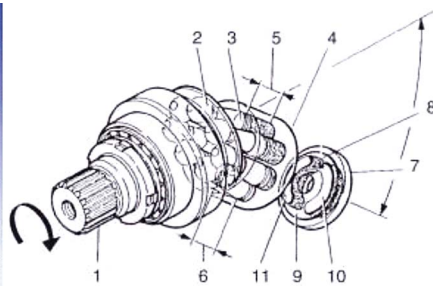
Нерегулируемая машина Bosch Rexroth с конусными поршнями (1 – приводной вал; 2 – поршни; 3 – поверхность поршней; 4 – ротор; 5 – ход нагнетания; 6 – ход всасывания; 7 – распределительный диск; 8 – верхняя мертвая точка; 9 – нижняя мертвая точка; 10 – серповидный паз напорной линии; 11 – серповидный паз всасывающей линии)
